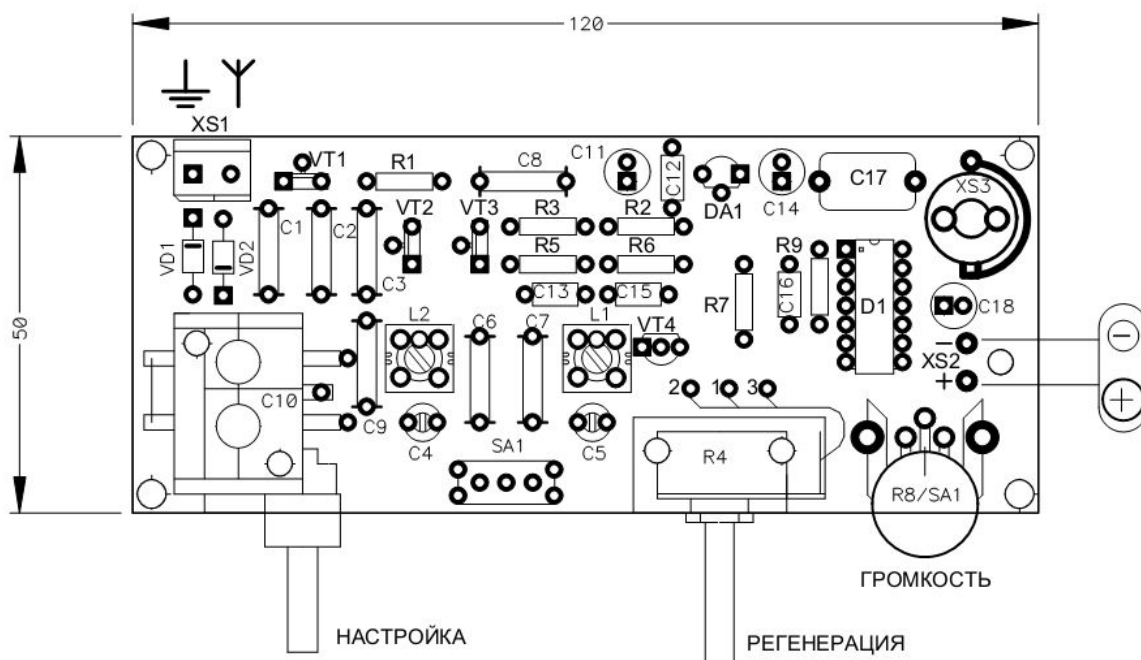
Сборочный чертеж платы (вид со стороны деталей).
